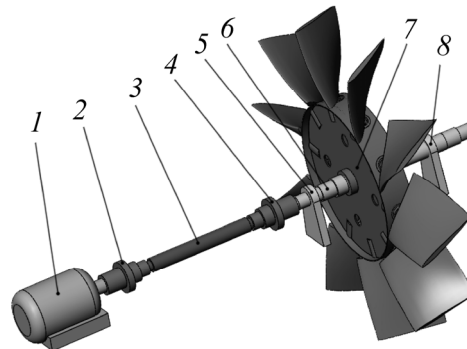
Схема ротора вентилятора главного проветривания: 1 — электродвигатель; 2, 4 — муфта; 3 — трансмиссионный вал; 5 — опора передняя; 6 — главный вал; 7 — рабочее колесо; 8 — опора задняя
